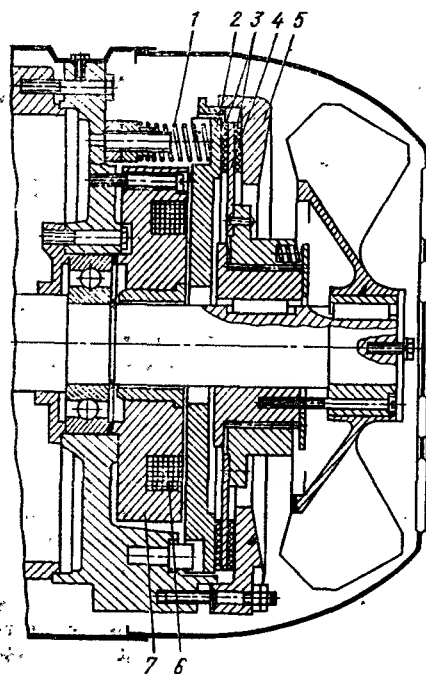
Тормозное устройство двигателя 4А160Е.
